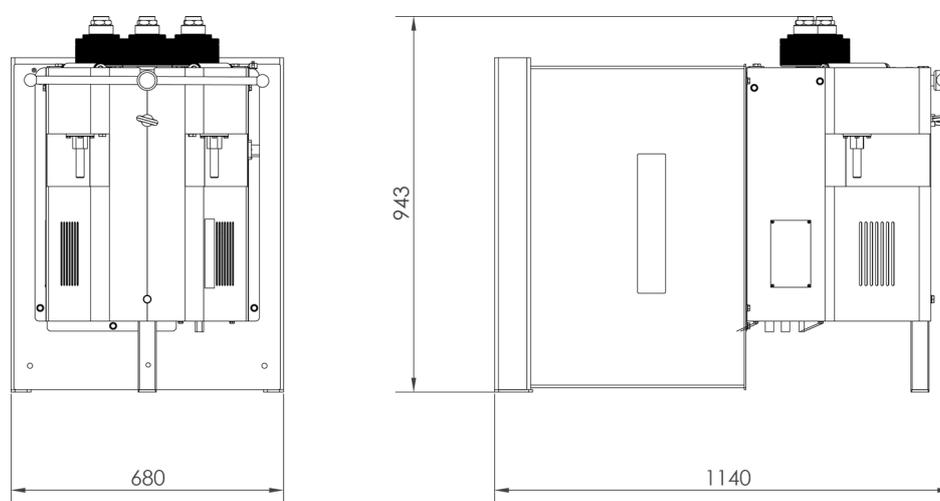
Dimensiones de la máquina con la bancada en posición horizontal
